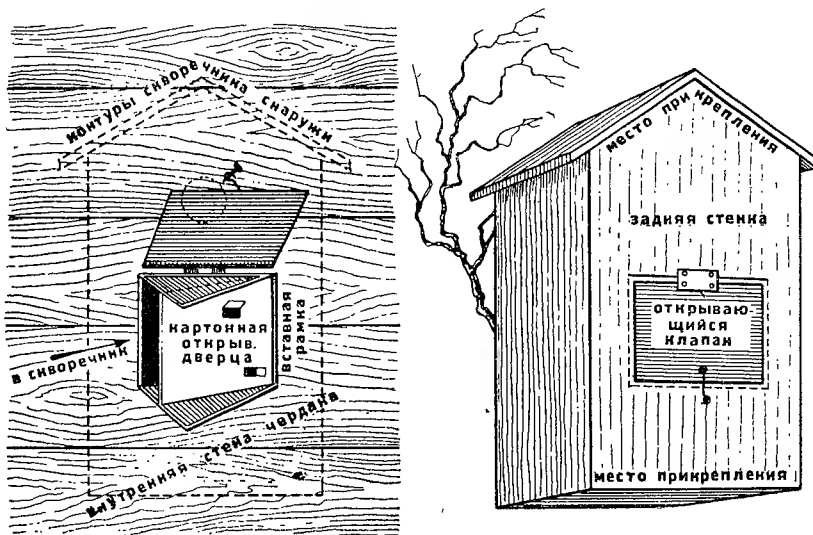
Детали устройства скворечника, открывающегося внутрь чердака (см. рис. 44)
